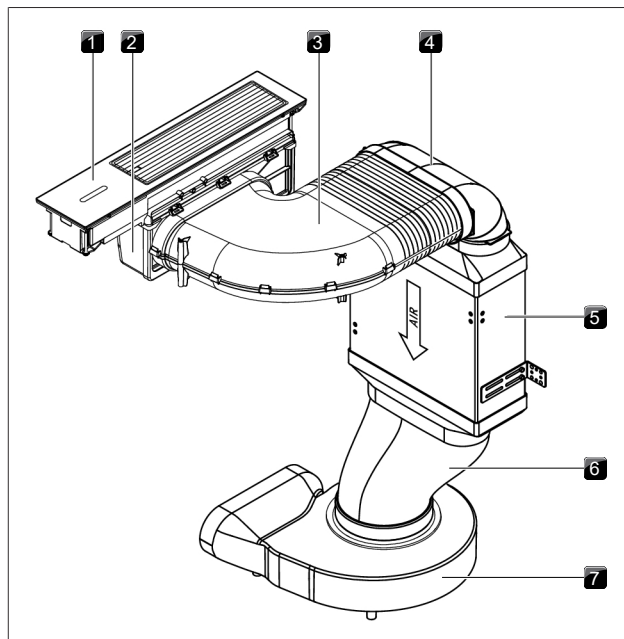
Esquema de montagem exemplificativo do exaustor de placa
